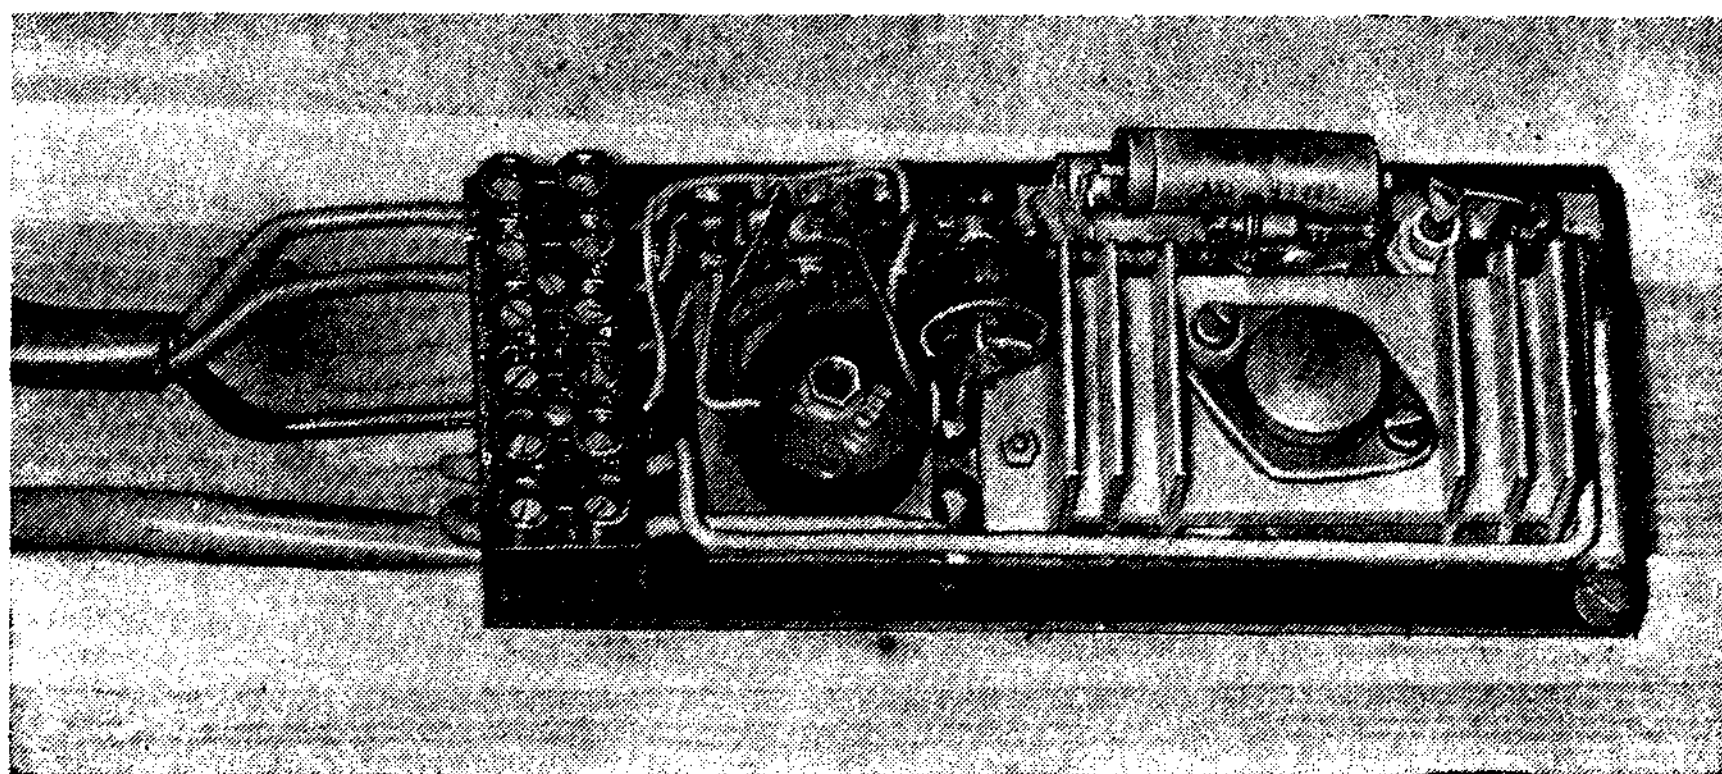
Zapojení měniče 12 V/220 V pro zářivku 8 W
